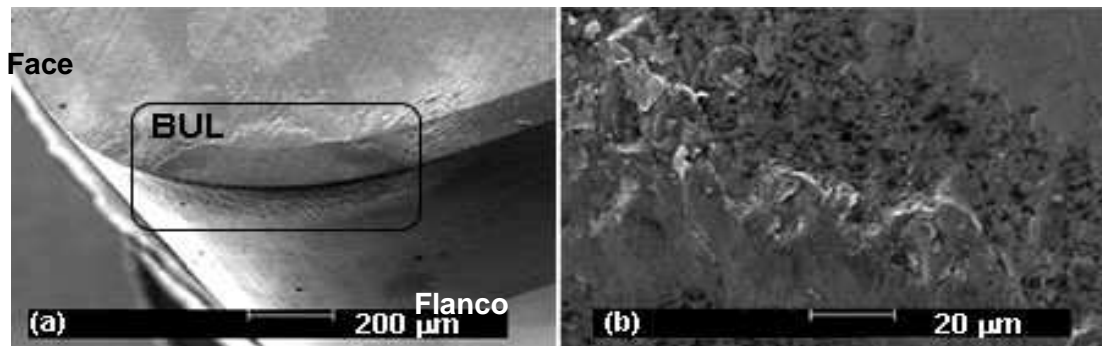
BUL na usinagem do ferro fundido cinzento com ferramenta de CBN a 800 m/min.
